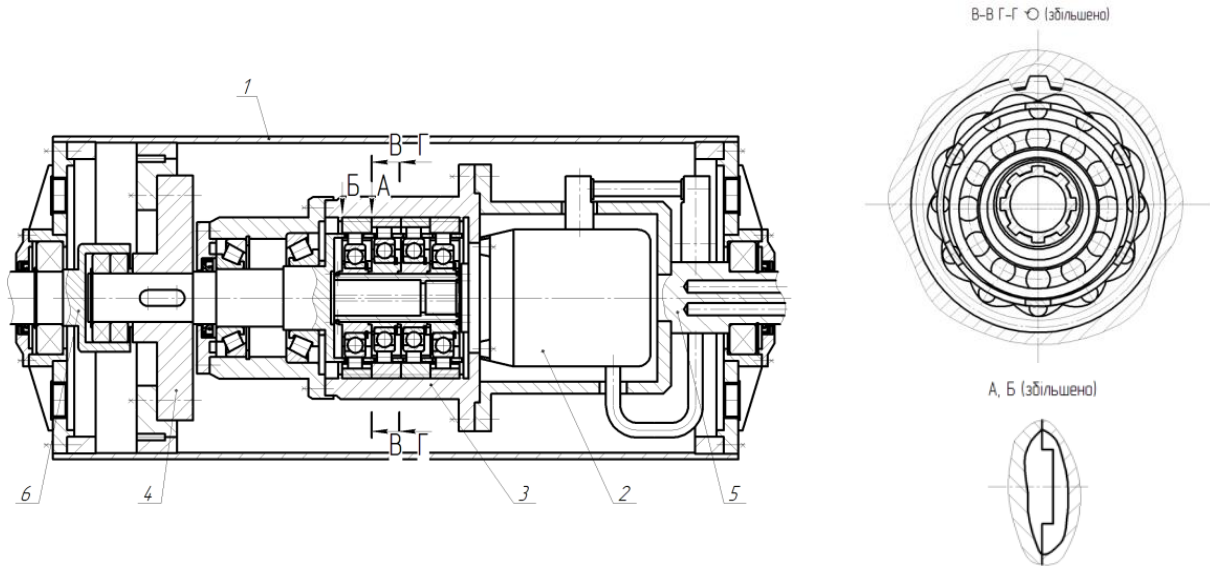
Конструктивна схема вмонтованого гідравлічного привода фрезерного барабана
